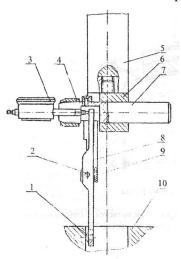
Приспособление для центрирования: 1 – упор; 2 – ось стойки; 3 – индикаторная головка; 4 – гайка; 5 – шпиндель; 6 – колодка; 7 – державка; 8 – рычаг; 9 – ограничитель; 10 – гильза
